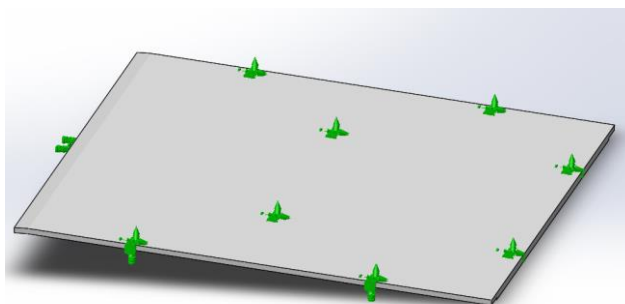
Vista de las sujeciones para cálculo por carga de nieve. Fuente: Propia.
